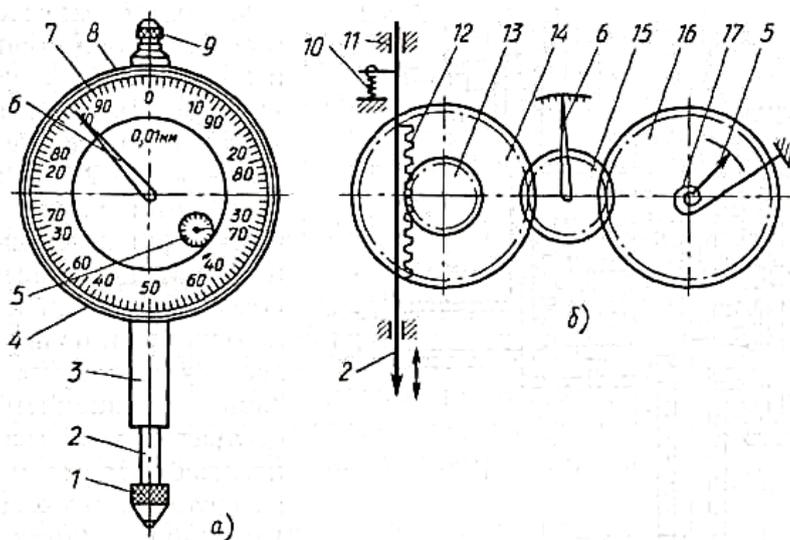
Индикатор часового типа: а) общий вид; б) схема прибора
